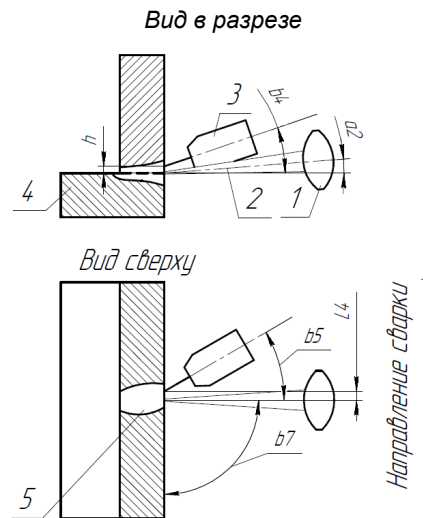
Схема ГЛДС, метод «Гибрид» углового сварного соединения в горизонтальном положении (РА):
